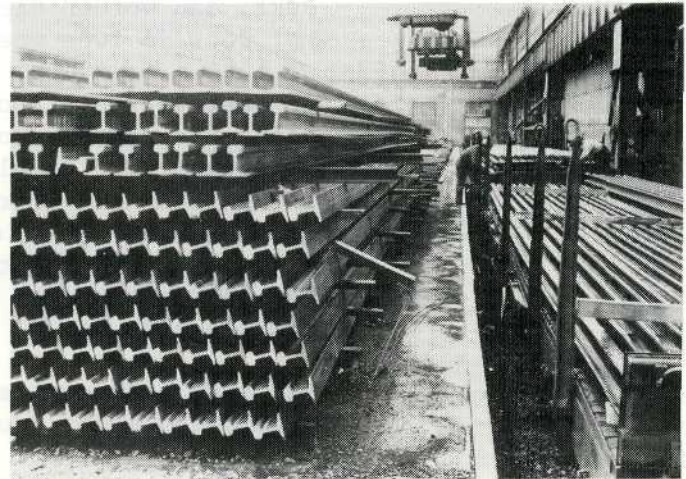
Voorbereiding van de lagen rails voor het eindonderzoek (Villerupt).
